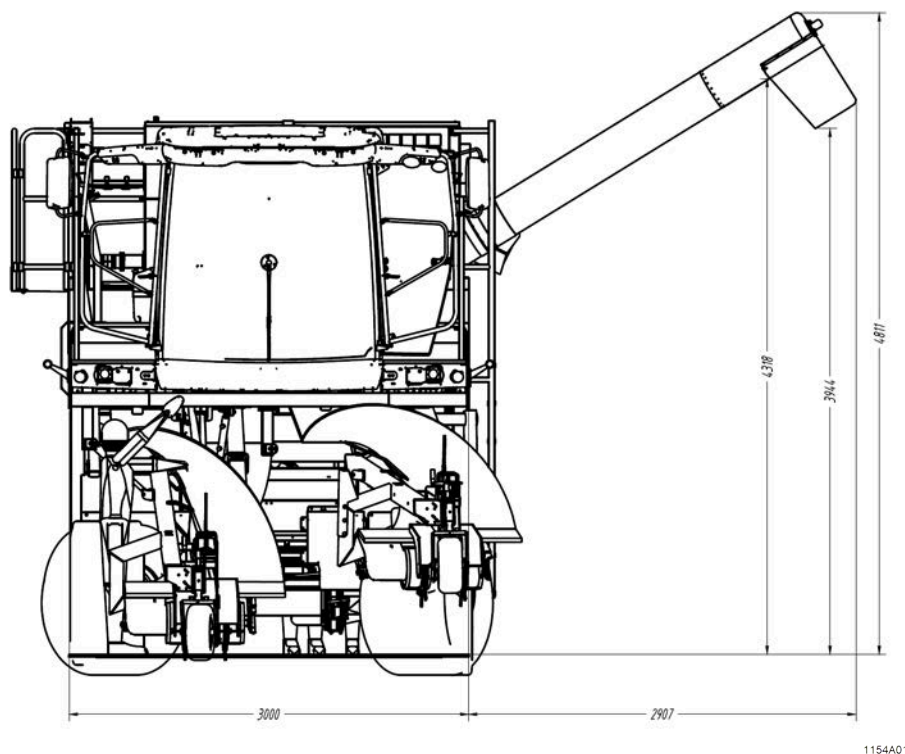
Dimensions de la machine avec tuyau de déchargement déplié
